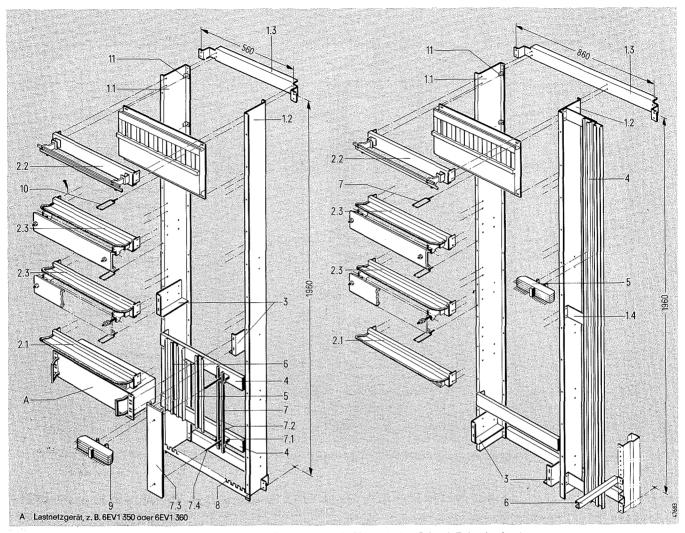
/3 Einbauteile für Schrank 8MF; links für 600 mm breiten Schrank, rechts für 900 mm breiten Schrank (Robustbauform)
